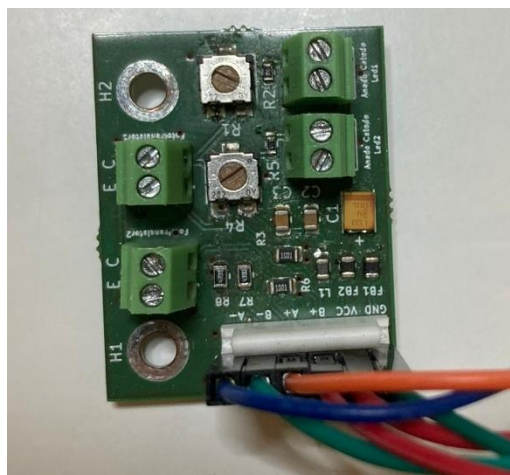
Circuito impresso já com componentes soldados.
